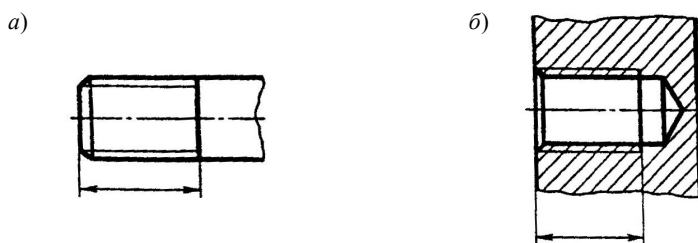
Обозначение размера длины резьбы с полным профилем:
